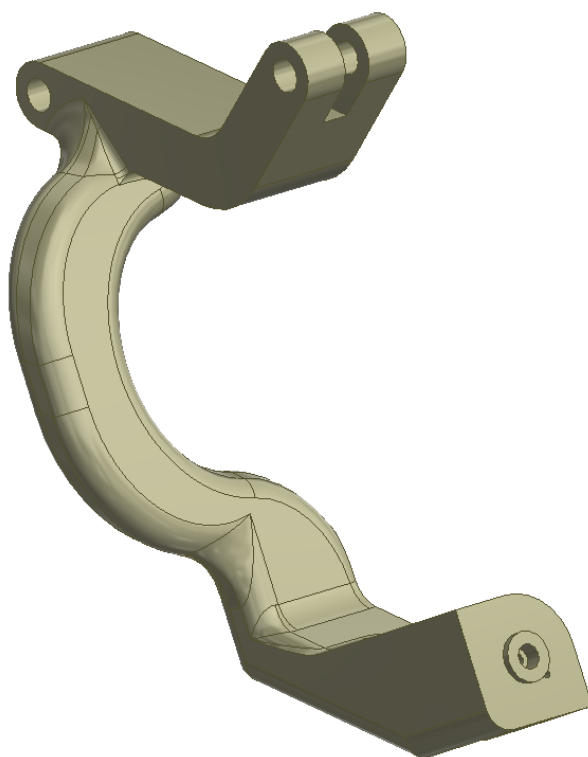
Přední nápravová tyč - díra pro připojení odpružení
